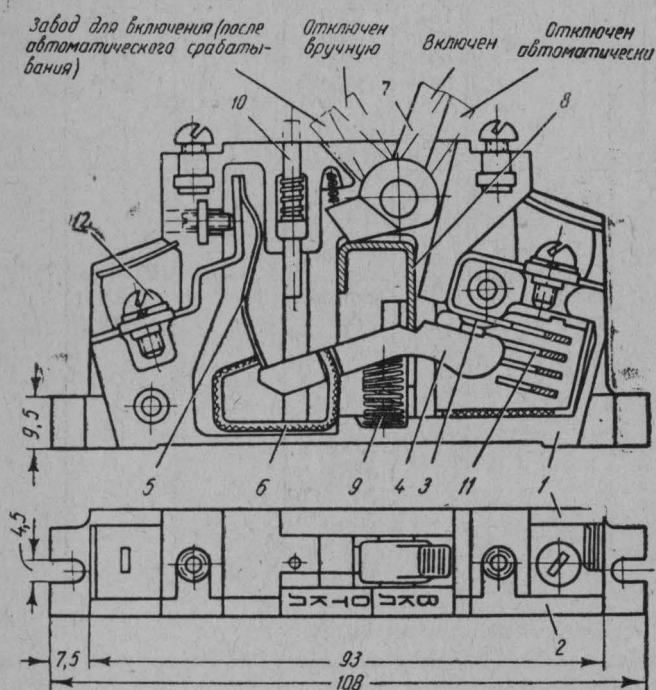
Кинематическая схема и габаритные размеры автомата АБ25
